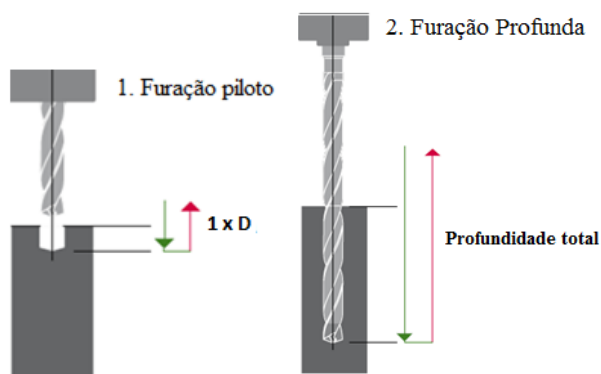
7 – Estratégias de usinagem utilizada nos testes.
